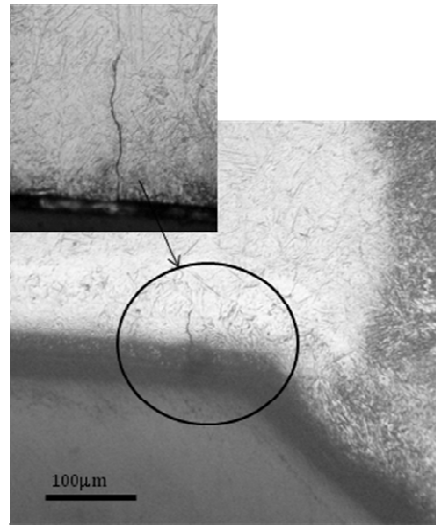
Microestructura en la zona del talón de la soldadura.
